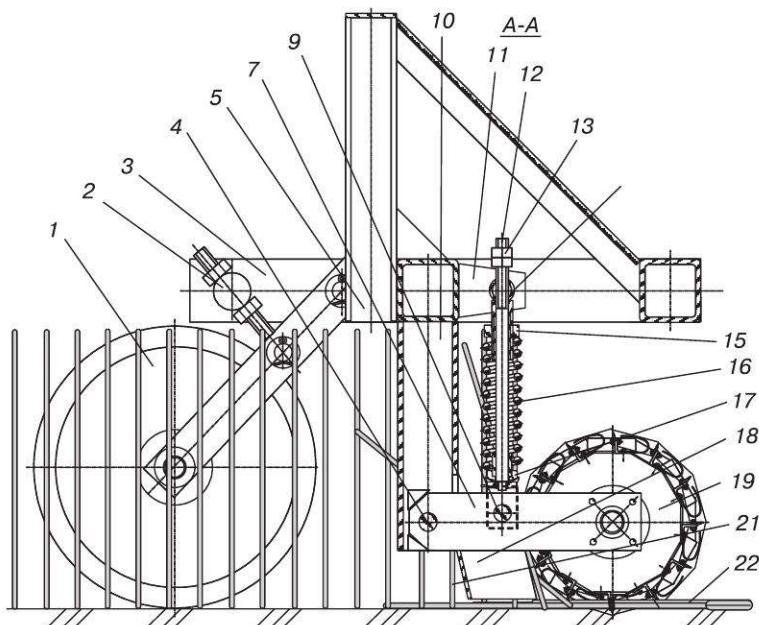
Різак-мульчувач рослин з барабанно-ножовими роторами (поздовжній розтин): 1 — опорне колесо; 2 — гвинтовий механізм регулювання висоти розташування рами; 3 — рама; 4 — палець важеля; 5 — начіпний пристрій; 6 — консоль; 7, 8 — важелі проміжної і бокової опори; 9 — палець гвинтової тяги; 10 — вертикальна стійка; 11 — щока провушини; 12 — гвинтова тяга; 13 — обмежувальна гайка; 14 — шарнір з кулісою; 15 — рухома чашка; 16 — пружина; 17 — нерухома чашка; 18 — подільник рослинної маси; 19, 20 — правий і лівий ротор; 21, 22 — стояча і порізана рослинна маса
